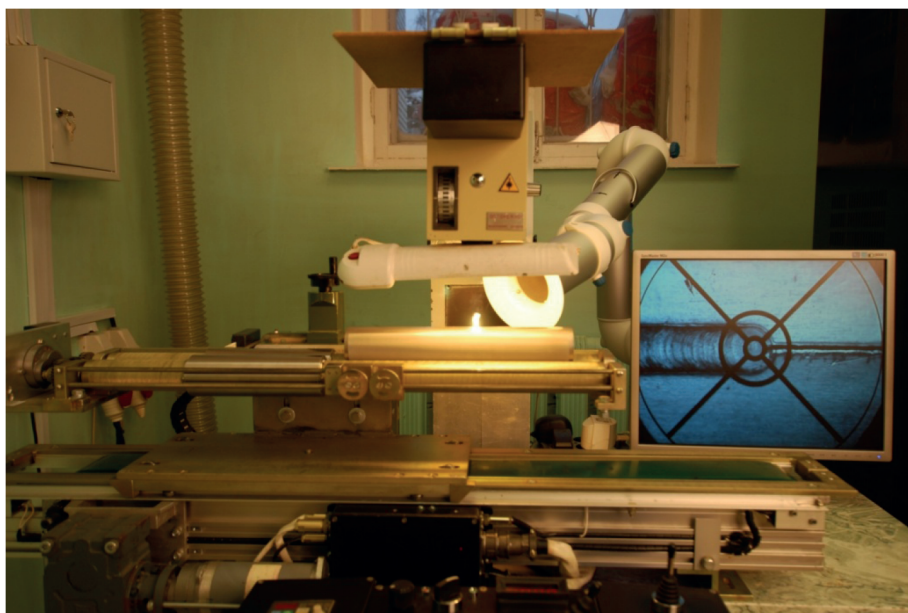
Базовая модификация технологической сварочной установки
